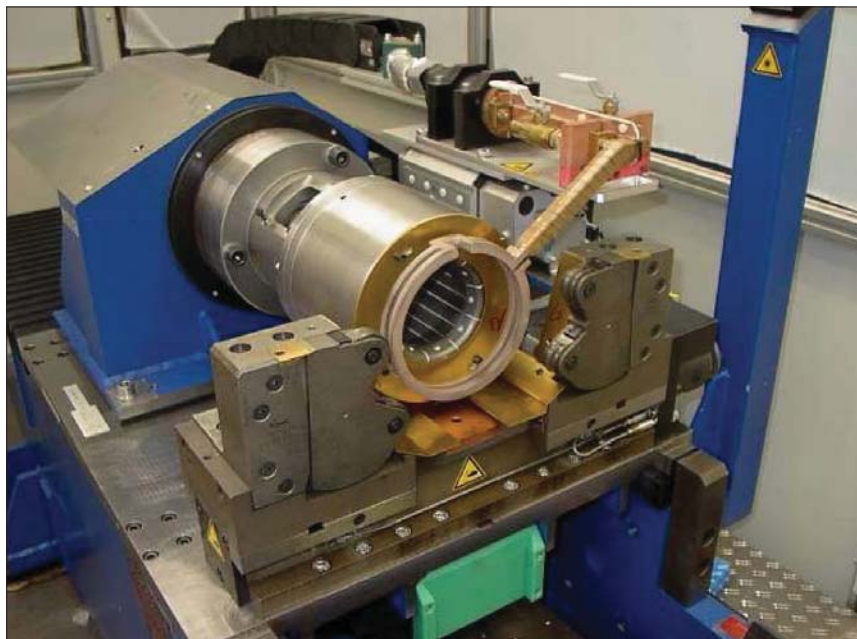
Particolare del sistema di fissaggio con dispositivo di riscaldamento induttivo
